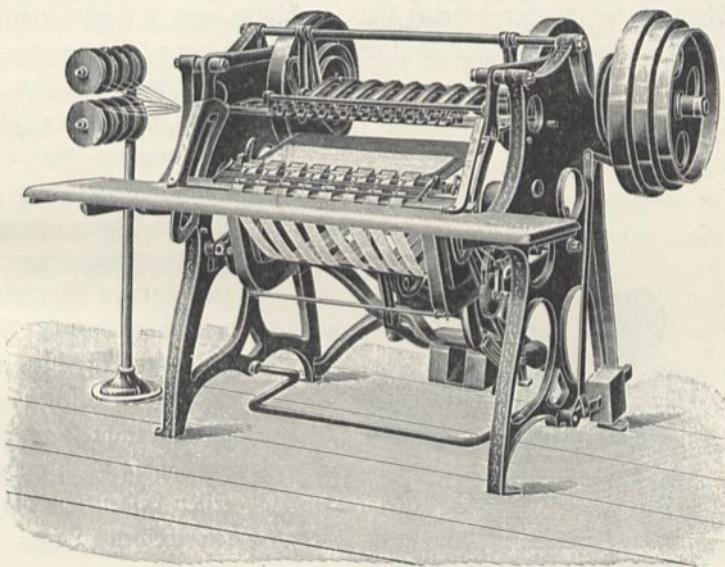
Drahtheftmaschine für Geschäftsbücher von Gebr. Brehmer, Leipzig-Plagwitz.
